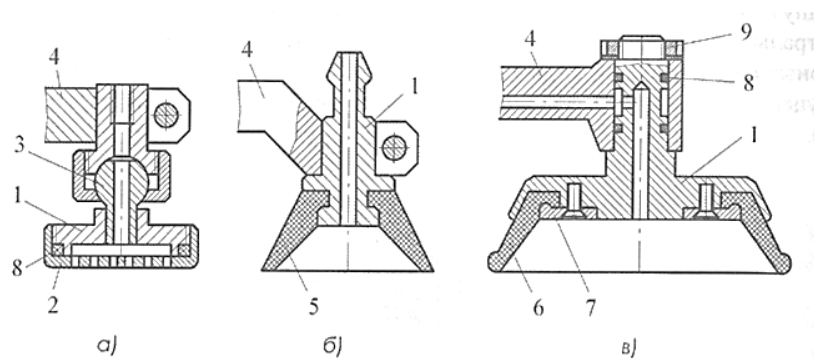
Конструкції вакуумних захватів: 1 – корпус; 2 – перфорована кришка; 3 – кульовий шарнір; 4 – рука автооператора; 5, 6 – гумові присмоктувачі; 7 – накладка; 8 – ущільнювач; 9 – гайка а – захват із жорсткою вакуумною камерою, б – захват невеликого розміру з еластичним ущільненням, в – захват великого розміру з еластичним ущільненням
